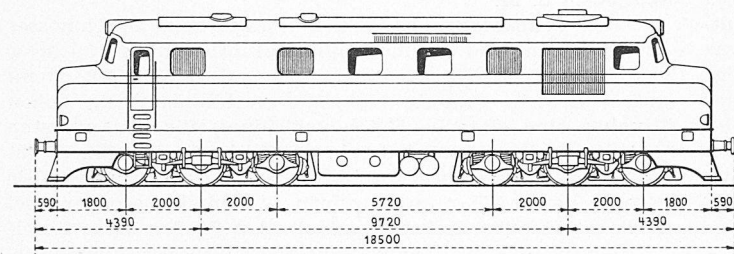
Typenskizze 1:200. — 1 Dieselmotor, 2 Generator, 3 Heizkessel, 4 Kompressor, 5 Ventilator, 6 Kühler, 7 Batterie, 8 Wasser
